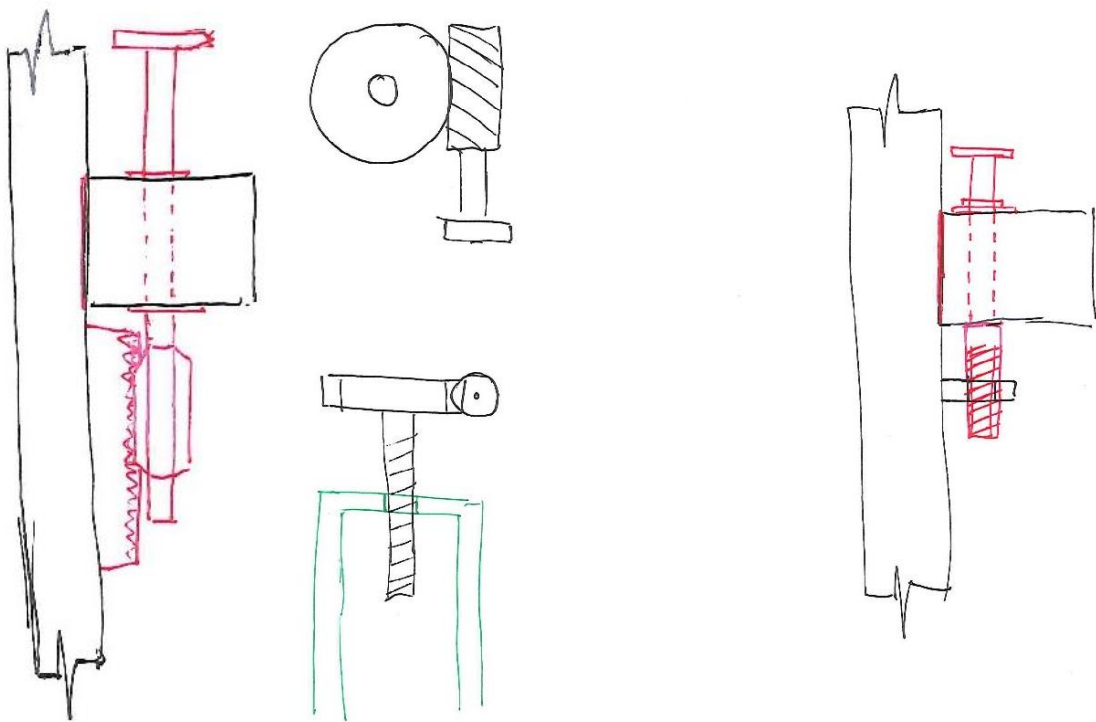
Skice principu fungování napínáku a uložení posuvného členu.
